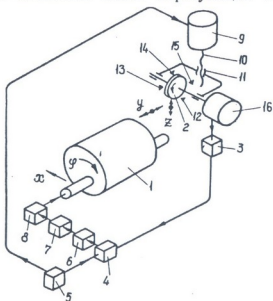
Схема шлифования зубьев некруглого цилиндрического колеса с применением ЧПУ
